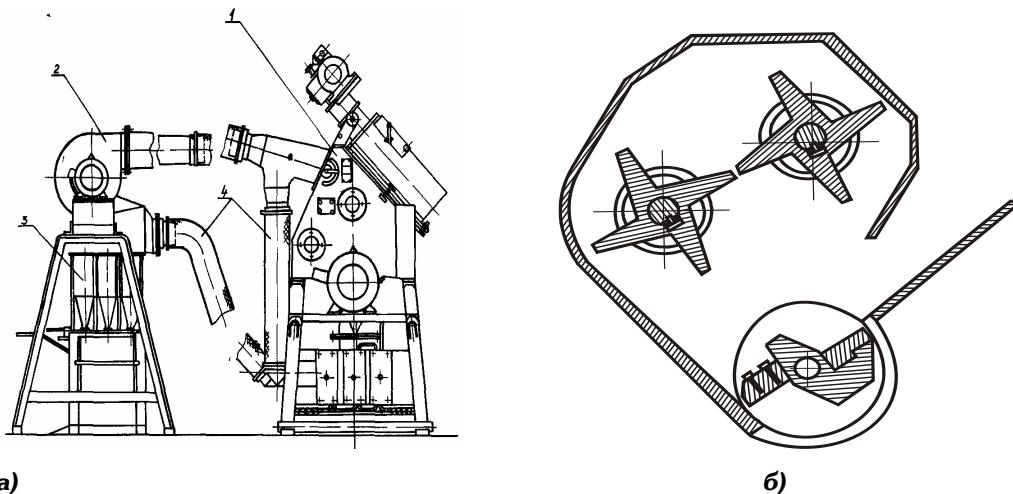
а) Общий вид установки «Комаровского» (УКОРП); б) Рабочая камера установки.
